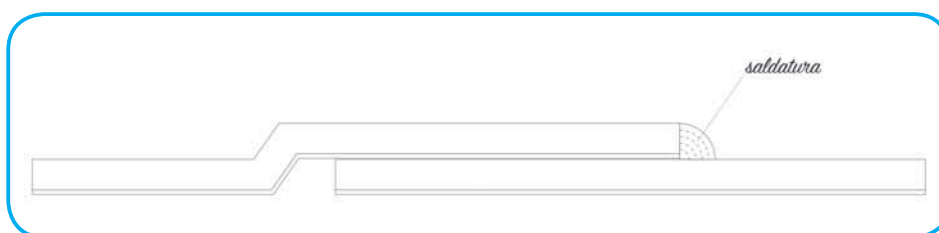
Positionnement de la soudure entre les éléments conducteurs
